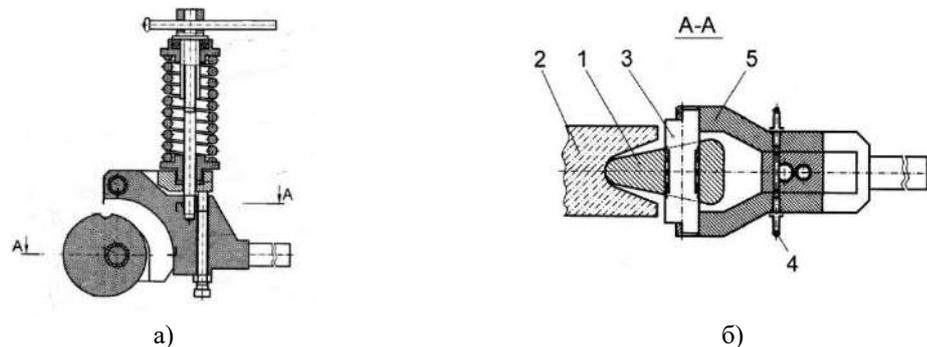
Конструкция для чистовой и упрочняющей обработки поверхностей валов сложного профиля: 1 – клиновой ролик; 2 – деталь; 3 – ось; 4 – рым-болты; 5 – рычаг (а – общий вид; б – роликовый узел)
